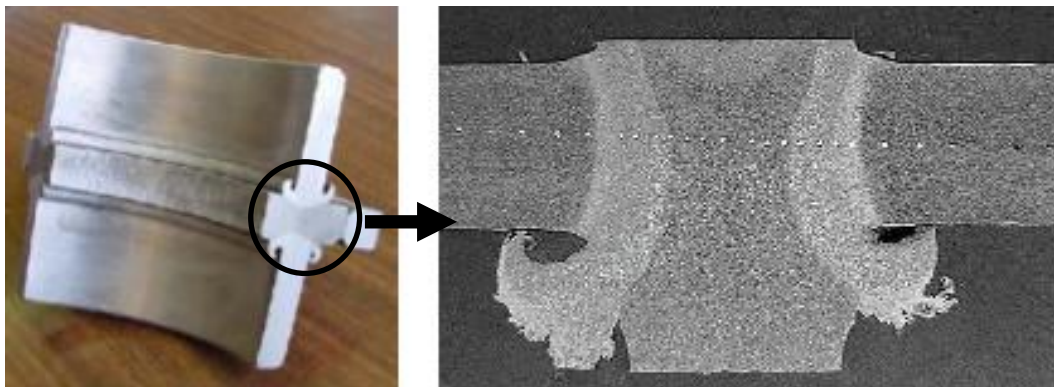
Amostra do tubo soldado por fricção e macrografia da solda (17).
